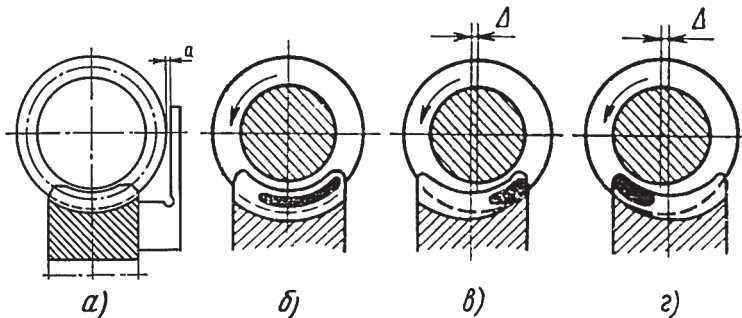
Схема установки и отпечатков на зубьях червячного колеса при проверке зацепления «на краску»:
